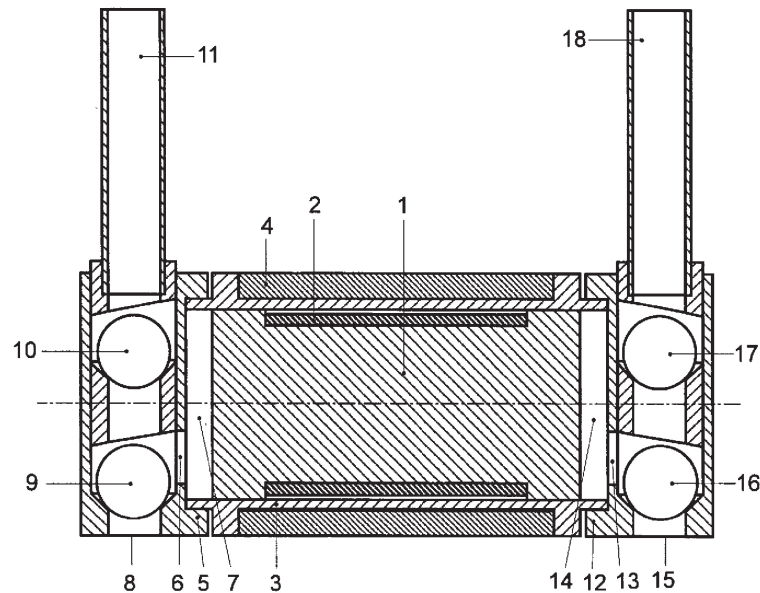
Prinzip einer elektrodynamisch, linear angetriebenen Pumpe [23]
